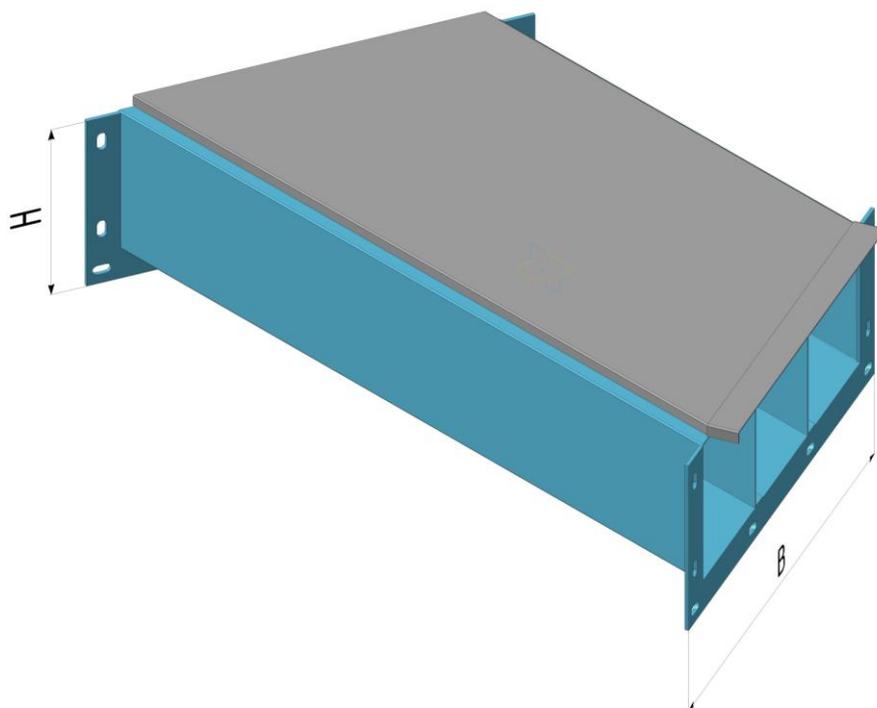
Короб кабельный блочный угловой горизонтальный плоский типа ККБ-УГП. Общий вид
